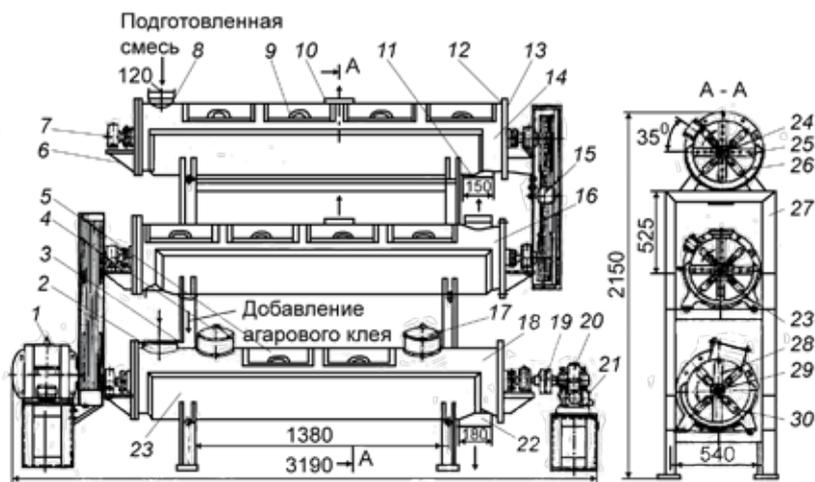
Трехкамерный взбивальный агрегат непрерывного действия К-18 для пастилы и зефира
